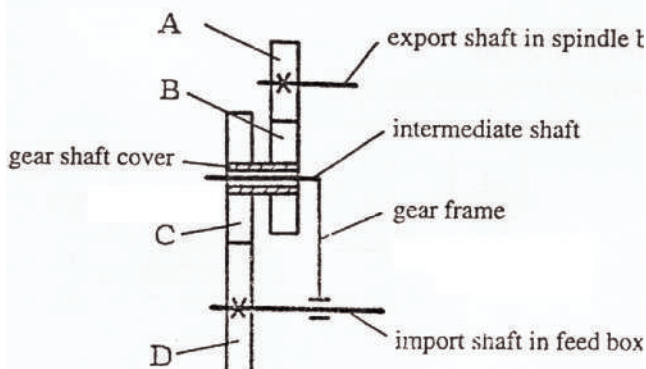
DIAGRAMA BOSQUEJO DE TRANSMISIÓN DE ENGRANAJES
